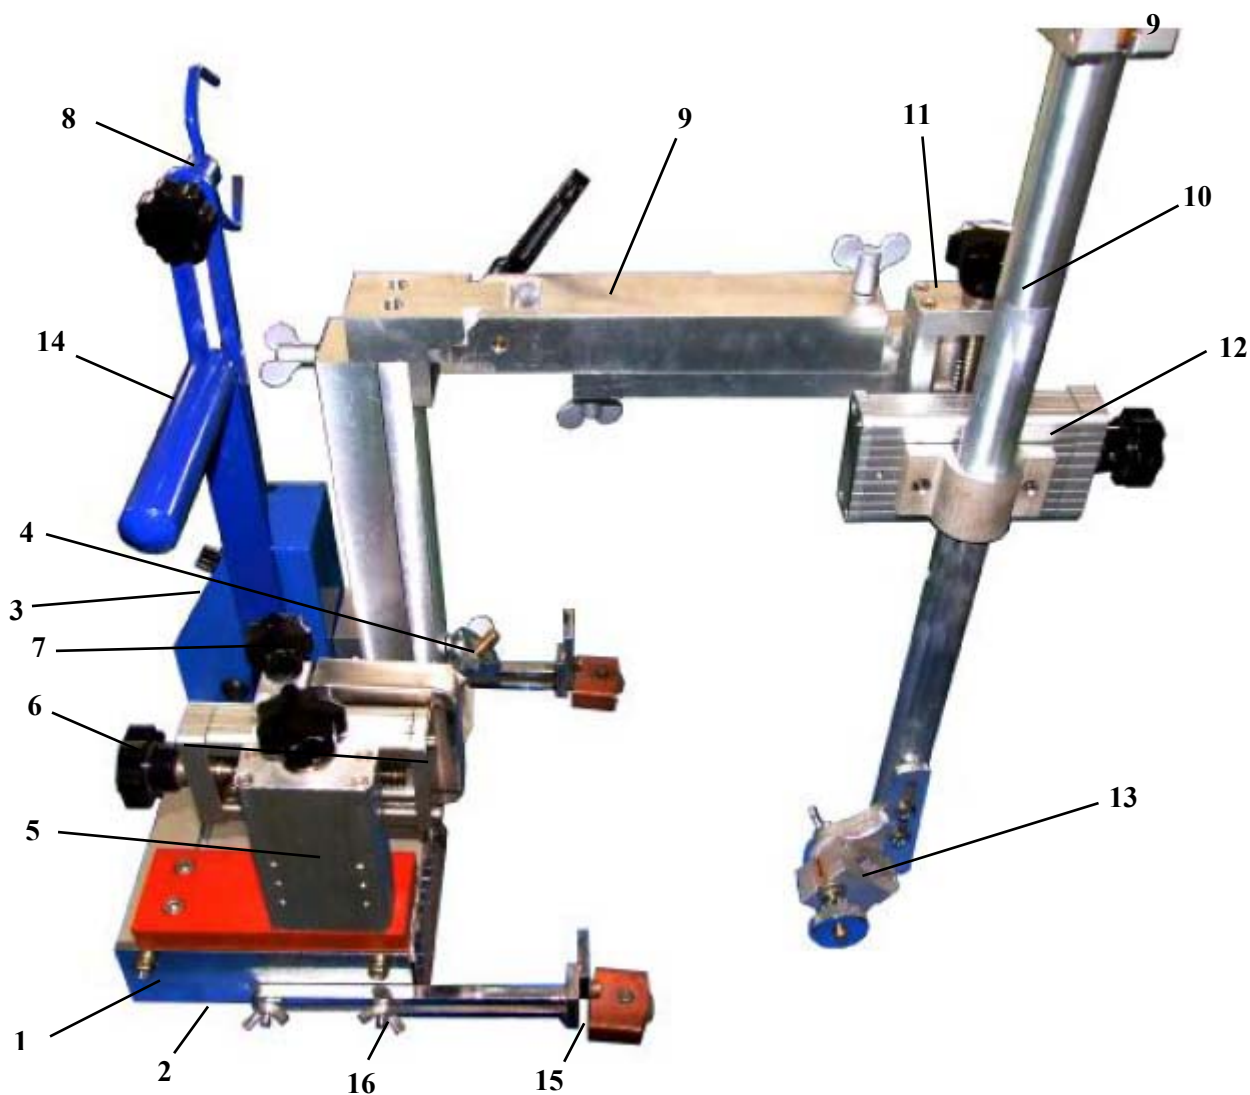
Сварочная каретка HIT-8SS HIF – внешний вид
